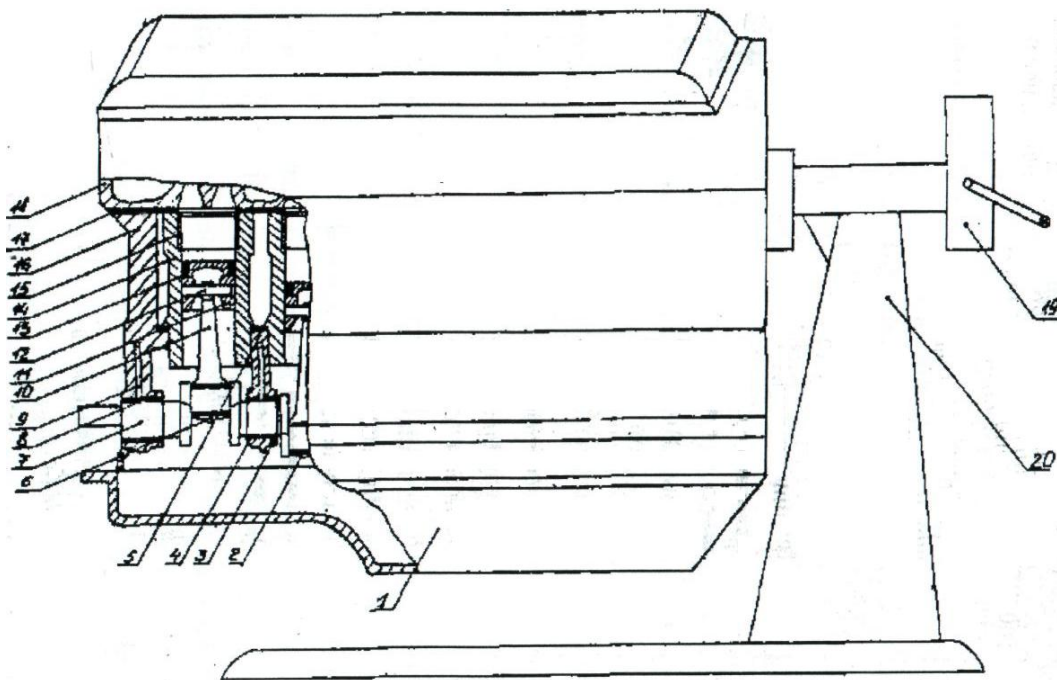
Установка для визначення параметрів рухомих деталей кривошипно-шатунного механізму:
